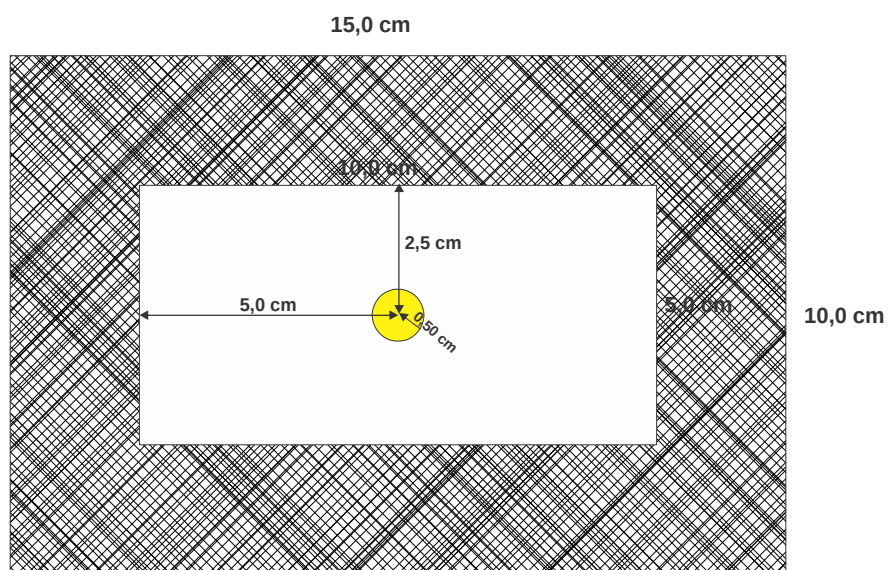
Diâmetro do furo de 1,0 cm – posição central
